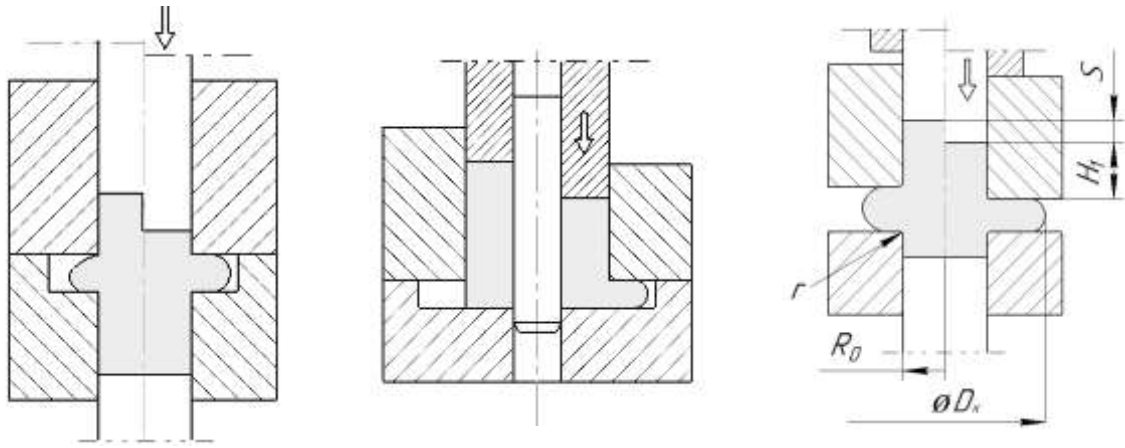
Схема радіального видавлювання деталей з фланцем
